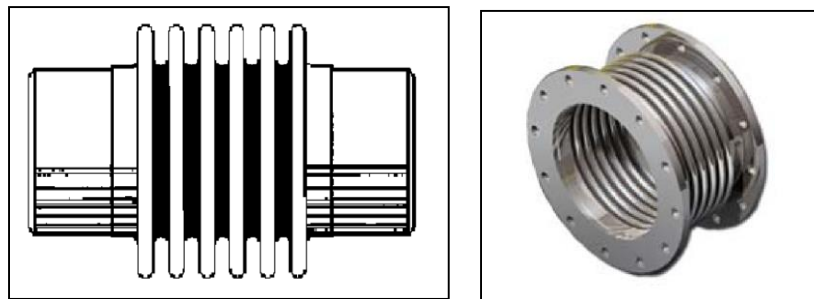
Junta de expansión Simple ("single expansion joint").
